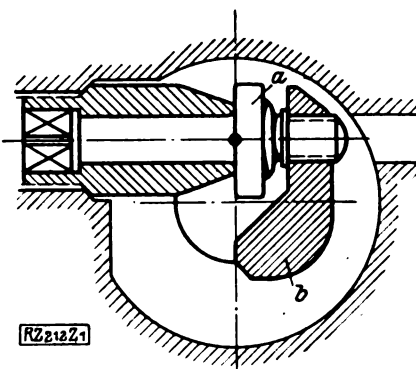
Schnellschlußventil für Wasserstandzeiger. *a* Ventilteller *b* Klappenarm.
